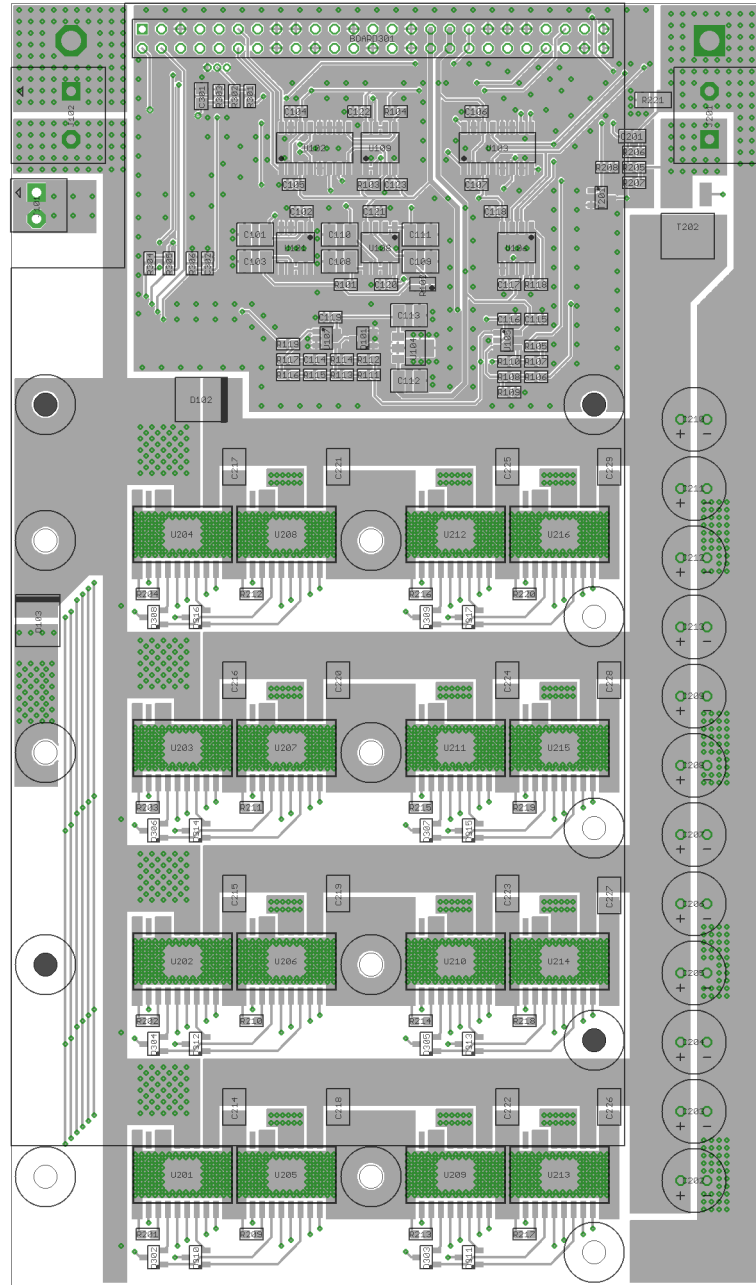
PCB Bauteilseite des *Power Board*.
